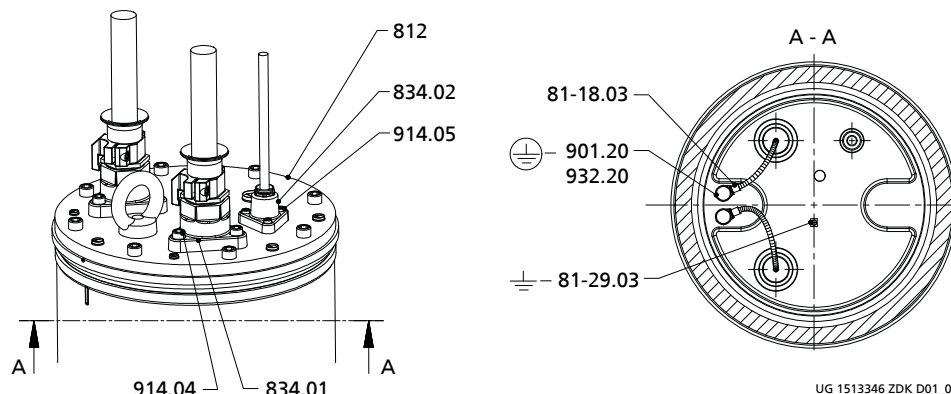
Демонтаж соединительного провода и кабельного ввода
